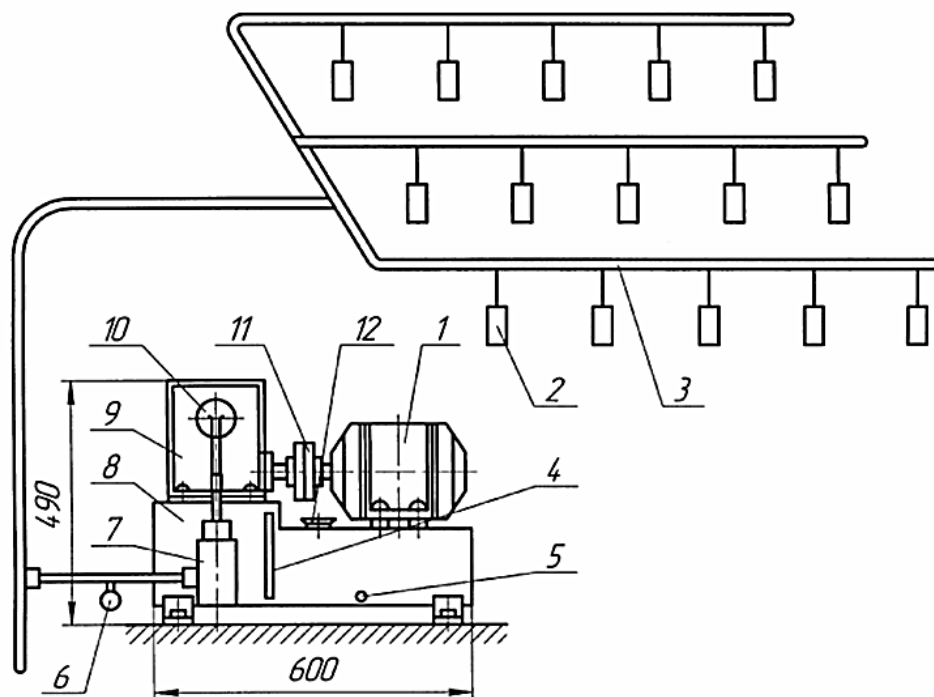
Схема установки для централизованной смазки группы кузнечно-прессовых машин
